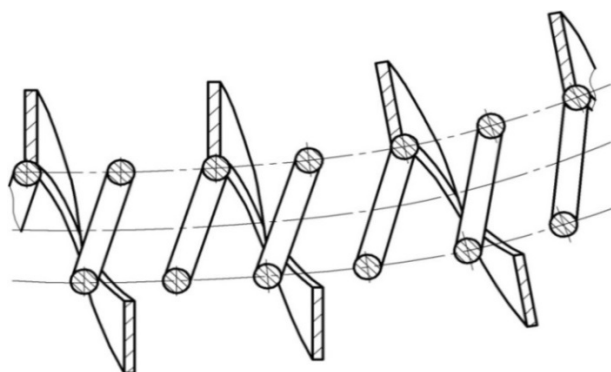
Робочий орган з прутковою несучою та смуговою робочою спіралями
